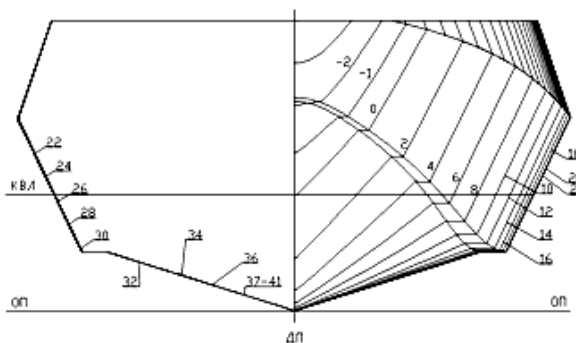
Проекция корпуса теоретического чертежа полуглиссирующего катера
